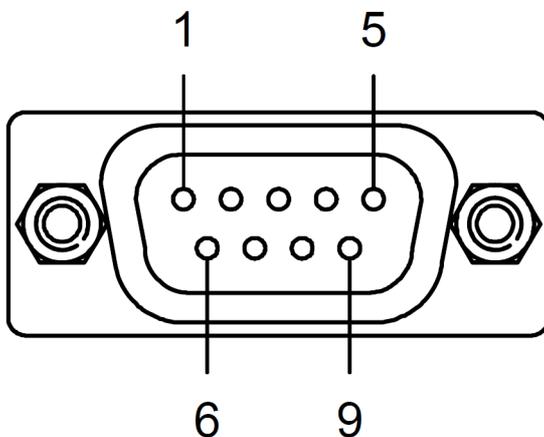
CBEB100.1-1m0 Steckverbinder
